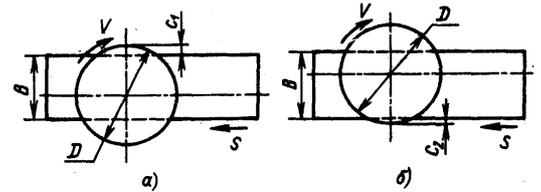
Расположение стальной заготовки при торцовом фрезеровании относительно фрезы: а — врезание зуба фрезы при $c_1 = (0,03 \div 0,05)D$; б — выход зуба фрезы при $c_2 = 0$
